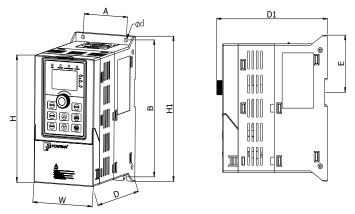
Внешний вид изделия30 kW G3, установочные размеры
